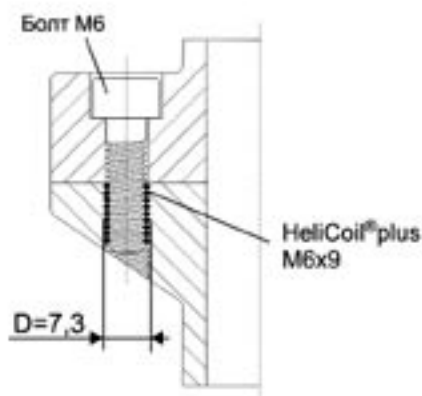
Ремонт резьбового отверстия с помощью резьбовой вставки HELICOIL®plus
